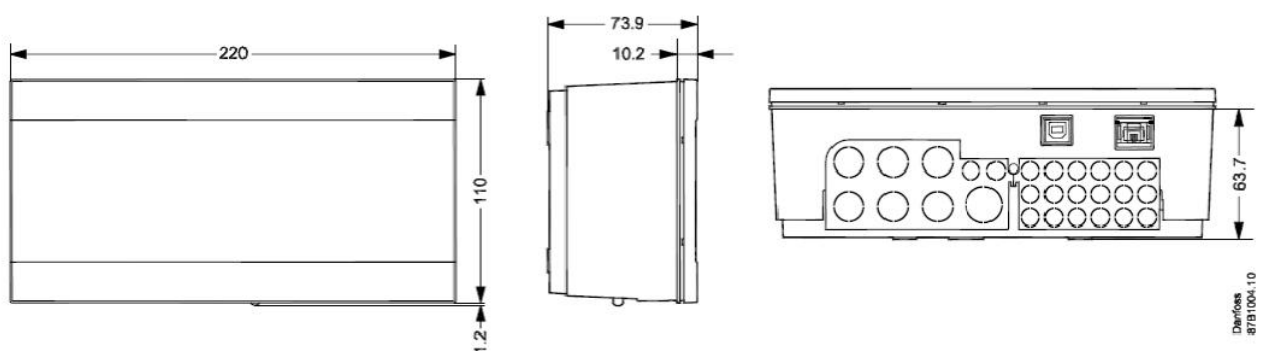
Габаритные и присоединительные размеры ECL Comfort 210B.
